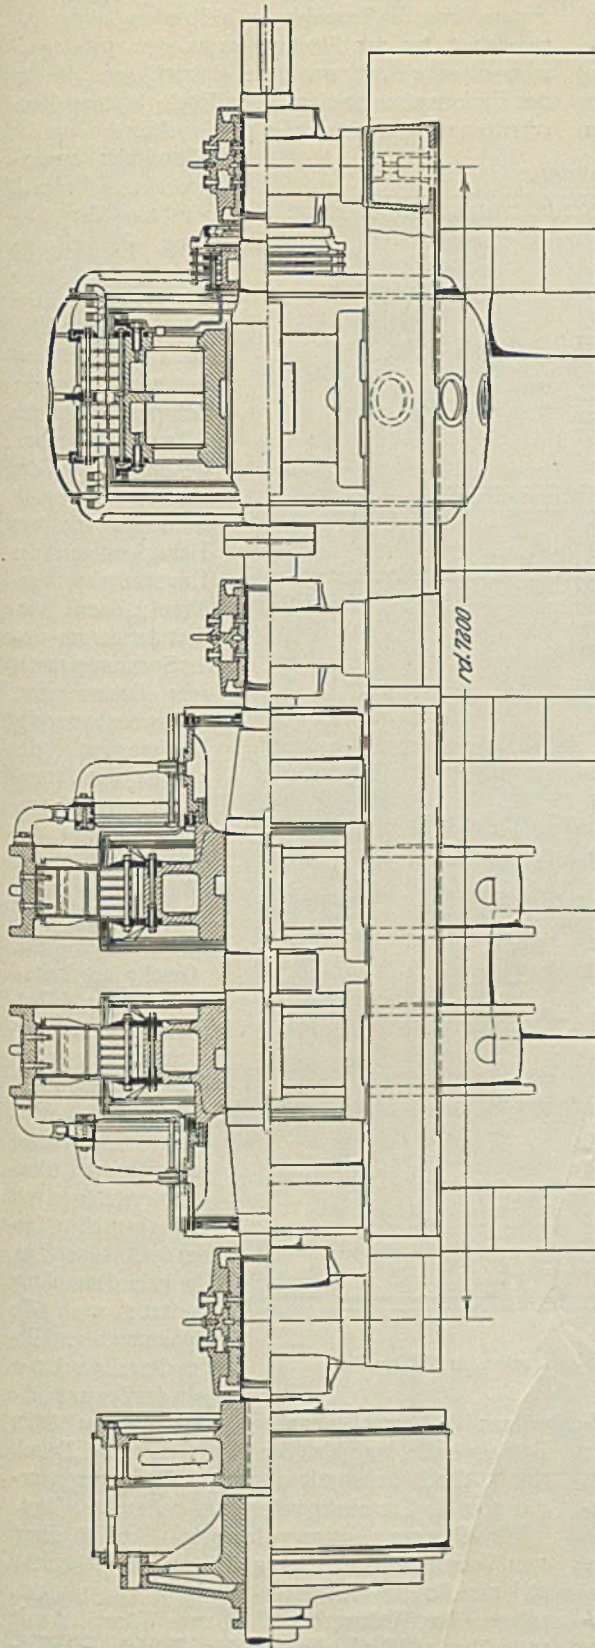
Schnitt durch einen Steuerungsumformer.
